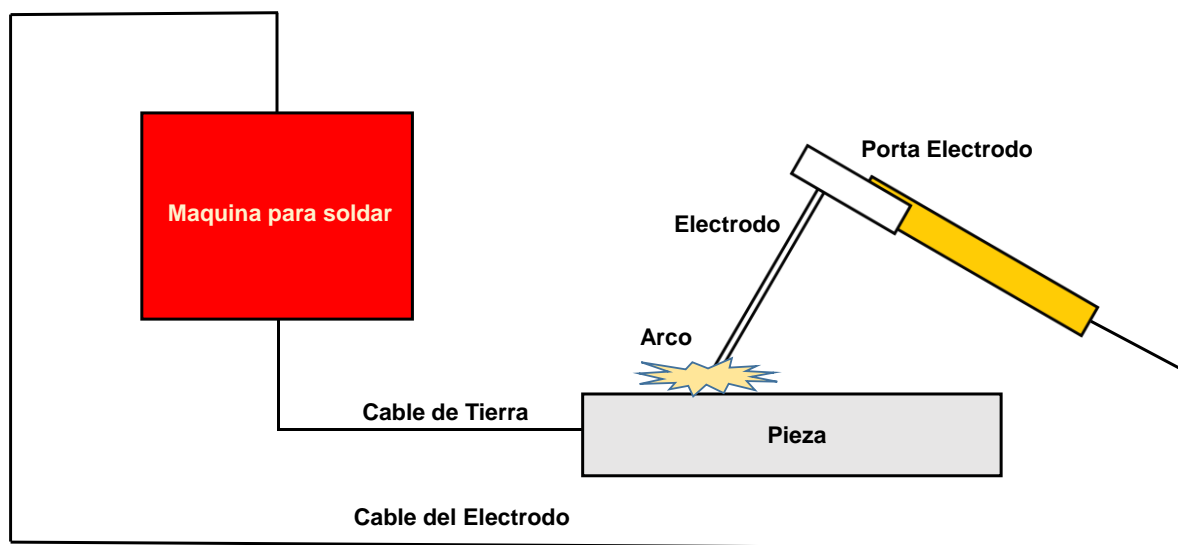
Esquema general del proceso de soldadura por arco eléctrico SMAW de soldadura metálica.
